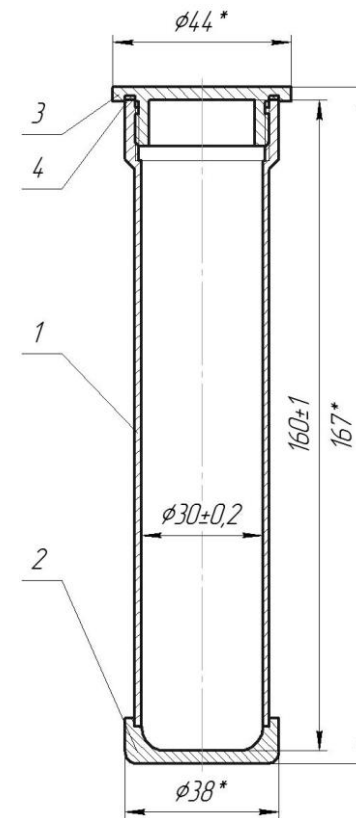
Сосуд высокого давления СВД : 1 – корпус; 2 – донце; 3 – крышка; 4 – уплотнение.
